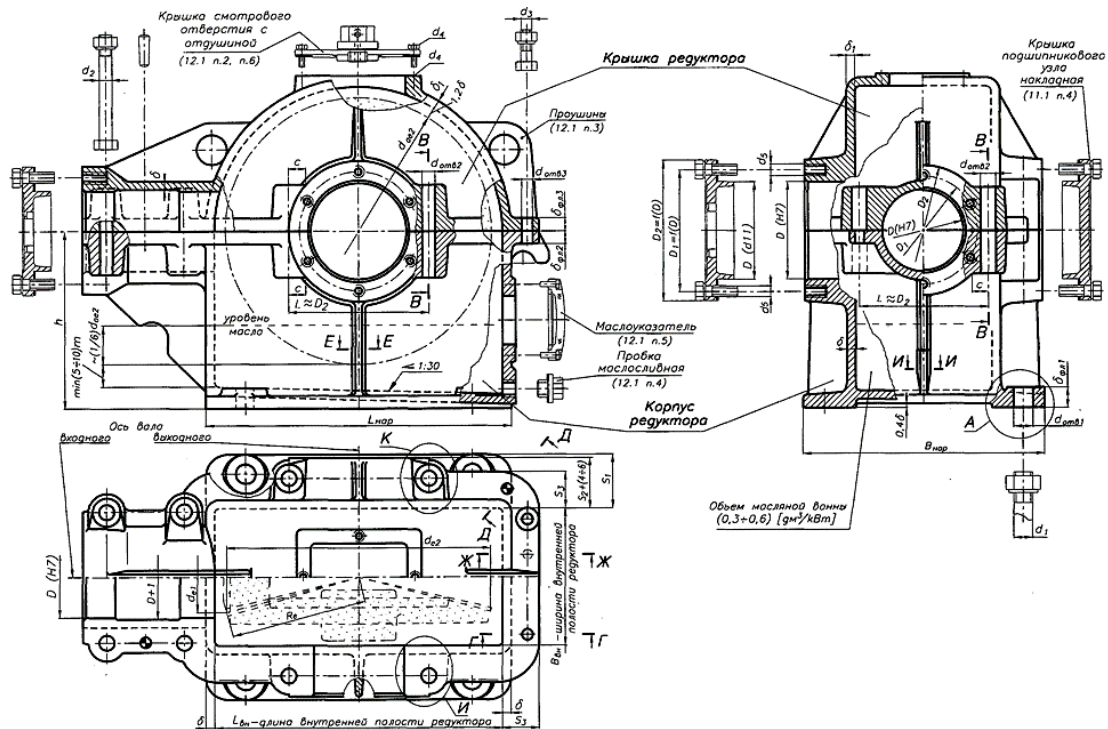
Корпус одноступенчатого цилиндрического редуктора
